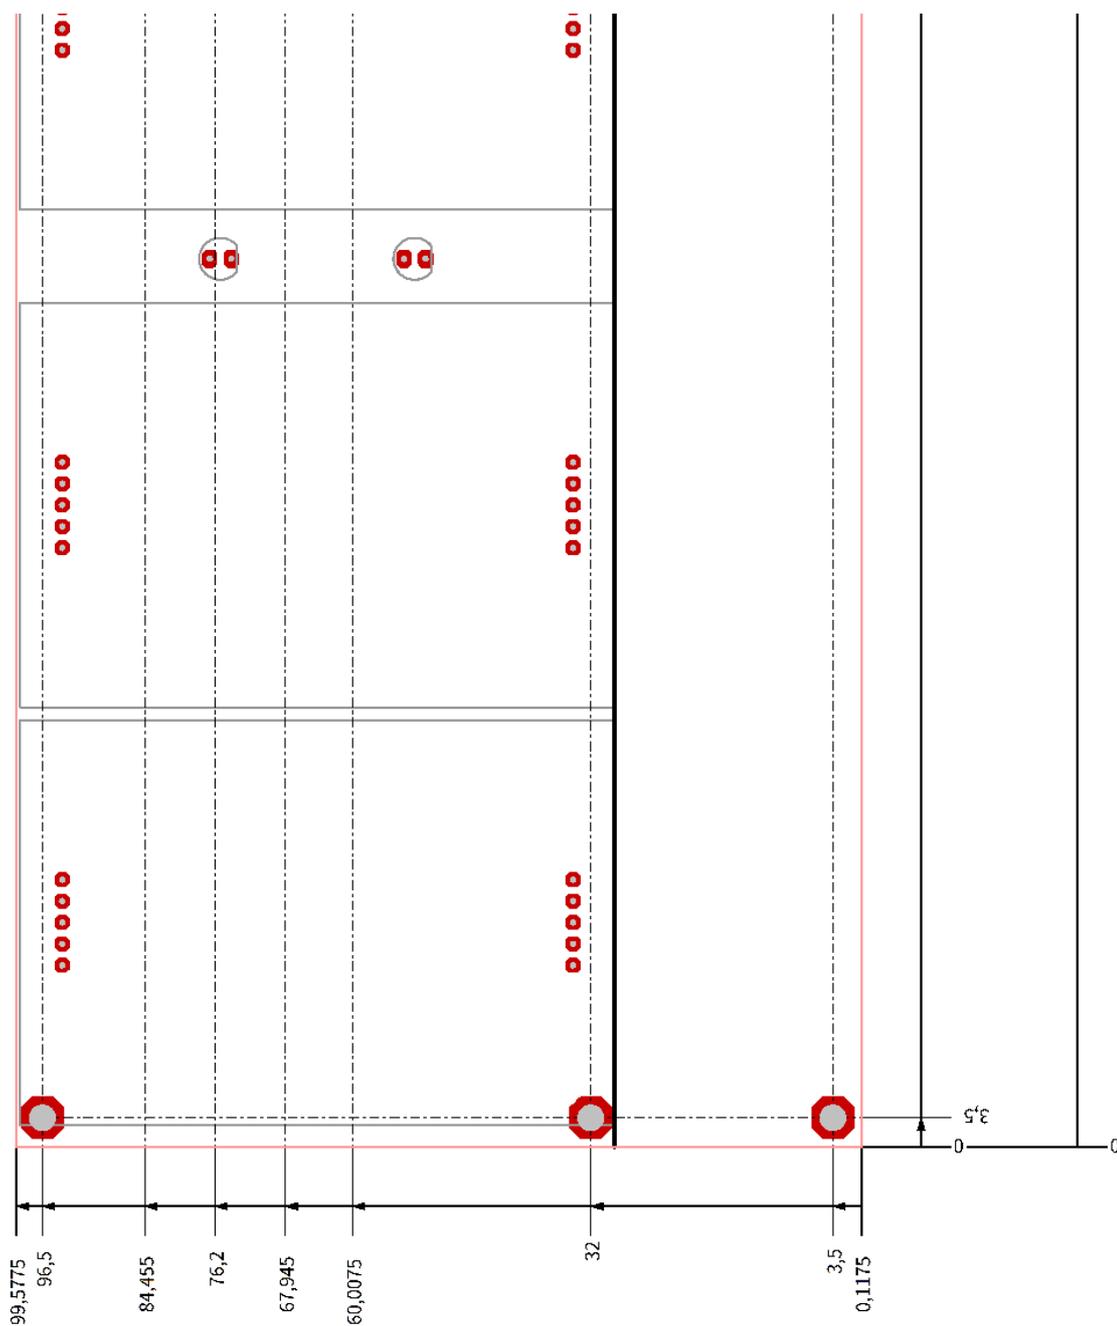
Beschreibung zum Einbau (Abmessungen) des Moduls PCB2399
